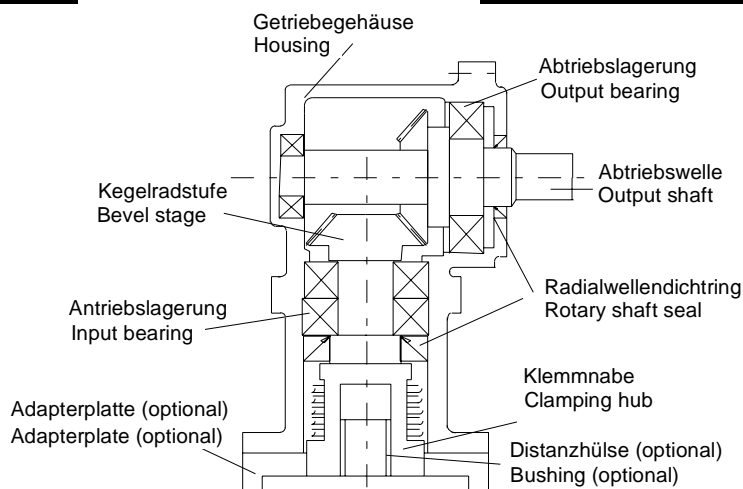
Aufbau des einstufigen Winkelgetriebes (SK)
